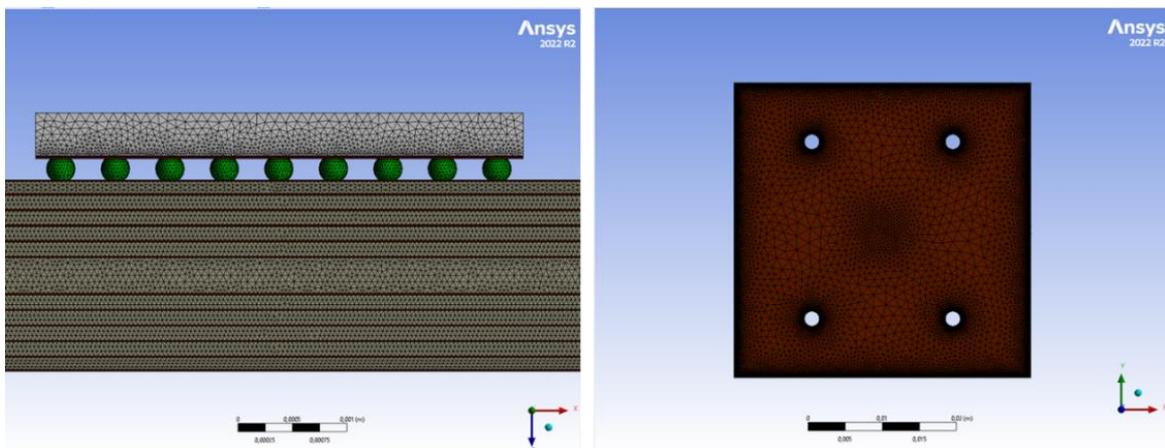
Maillage du VT4x4 RIC assemblé sur PCB multicouche
